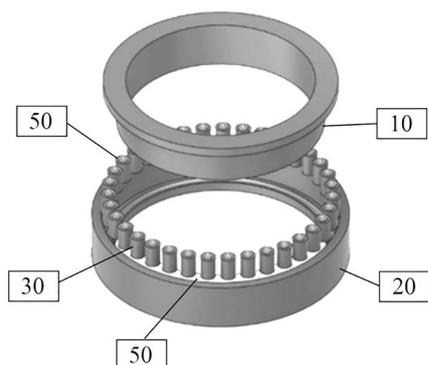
3D-модель модернизированного радиального подшипника с роликовыми цилиндрическими телами качения
